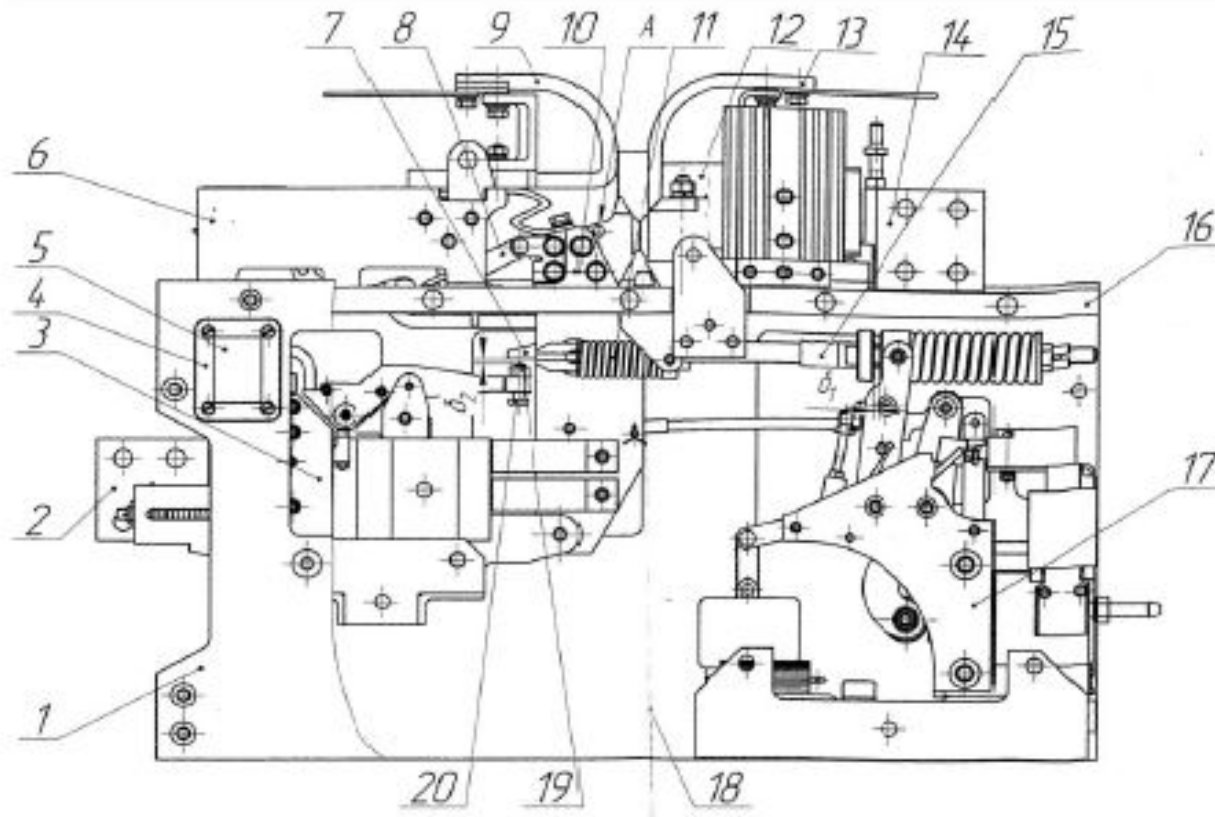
Общий вид быстродействующего выключателя ВАБ-55
